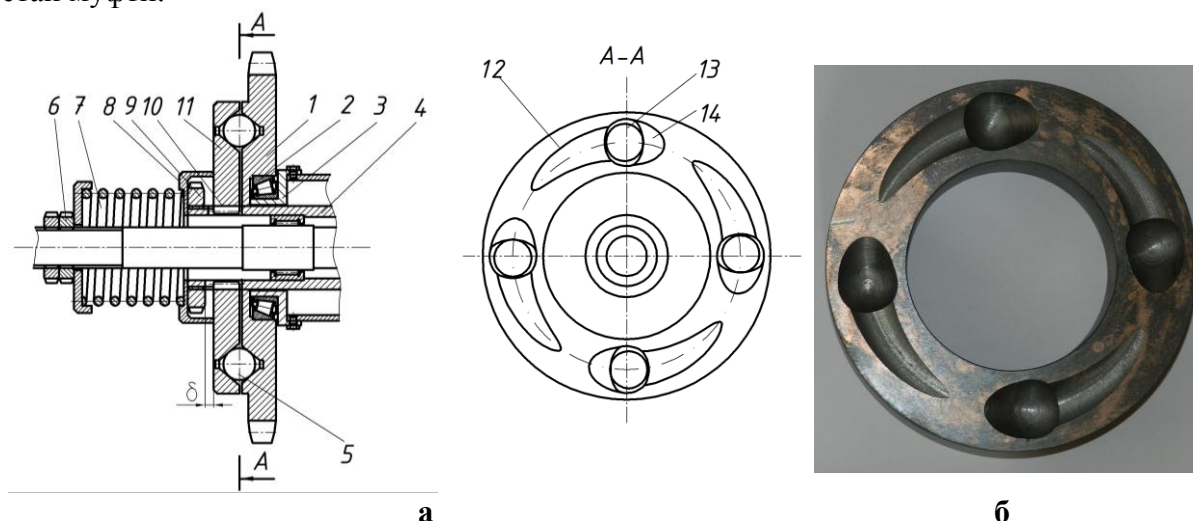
Конструктивна схема запобіжної муфти (а) та загальний вигляд робочої поверхні веденої півмуфти (б): 1 – ведуча півмуфта; 2 – радіально – упорний підшипник; 3 – корпус; 4 – вал шнека; 5 – кульки; 6 – гайка; 7 – цент-ральна пружина; 8 – втулка; 9 – гайка; 10 – шліци; 11 – ведена півмуфта; 12 – похила робоча канавка; 13 – лунки; 14 – похила зворотна канавка
